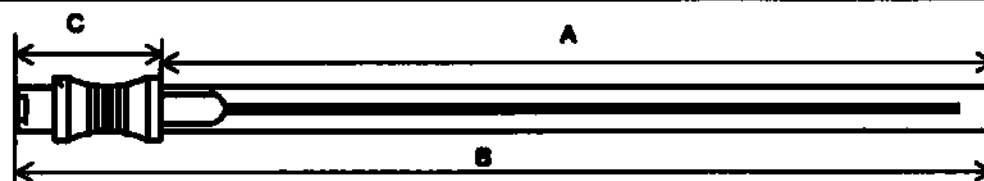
Схематичный чертёж инструмента для введения / Fig. 7 Structure of Insertion tool
